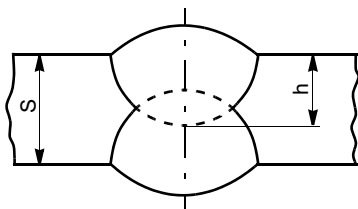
Вид сварного соединения с двусторонними швами
